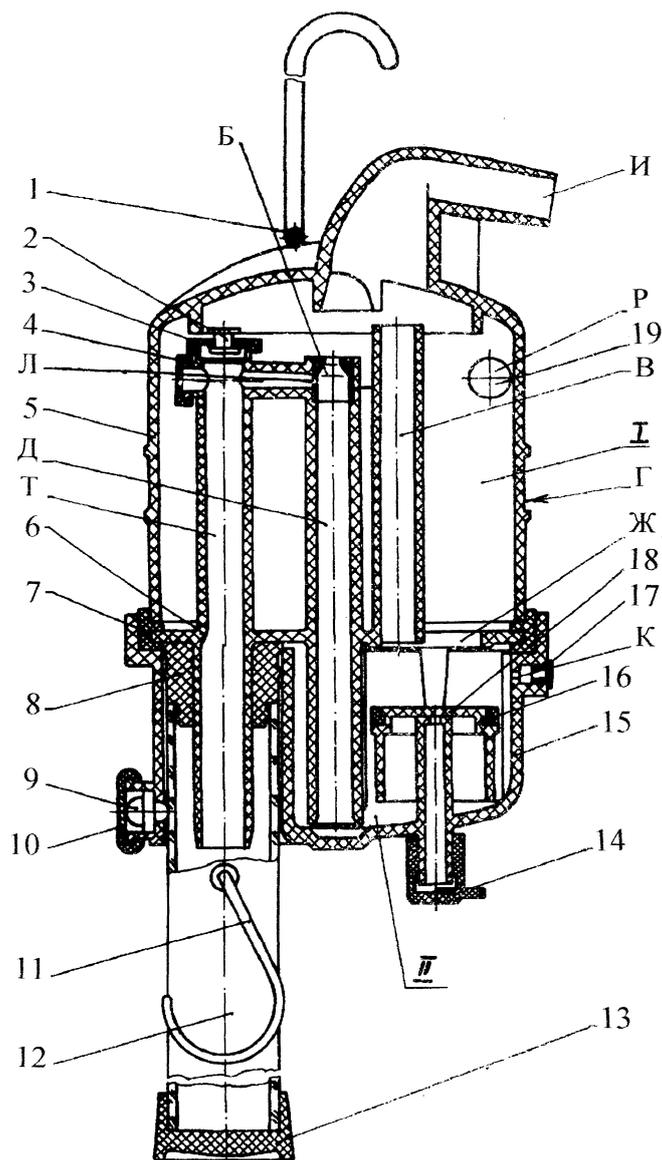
Общий вид устройства УЗМ-1А в разрезе:
